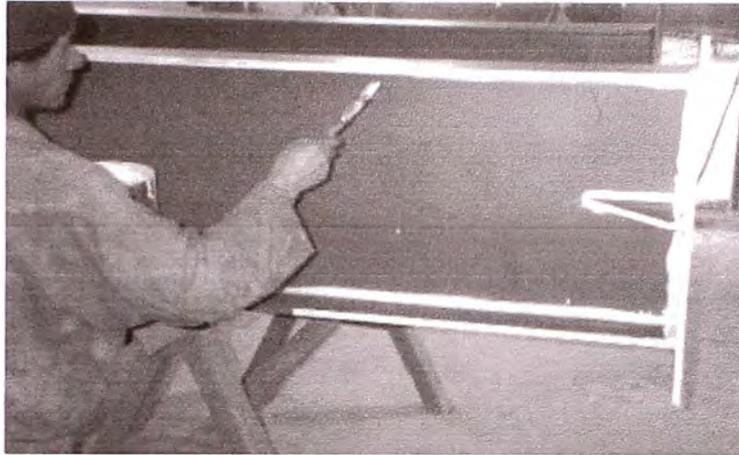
Cordoneo o Stripe coat para reforzar las zonas más propensas a corrosión
